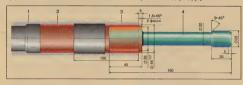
Запрессовка втупок: 1 - труба; 2, 3 - втупки; 4 - оправка для запрессовки втупок.
